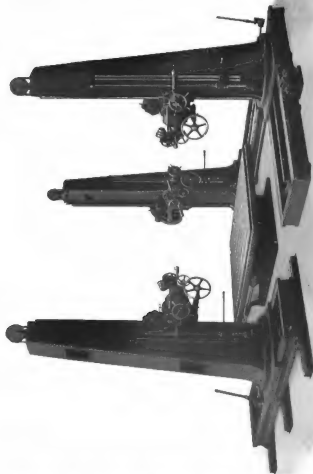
Dreifache Stahlkesselbohrmaschine (Werkzeugmaschinenfabrik Collet &amp; Engelhardt).
